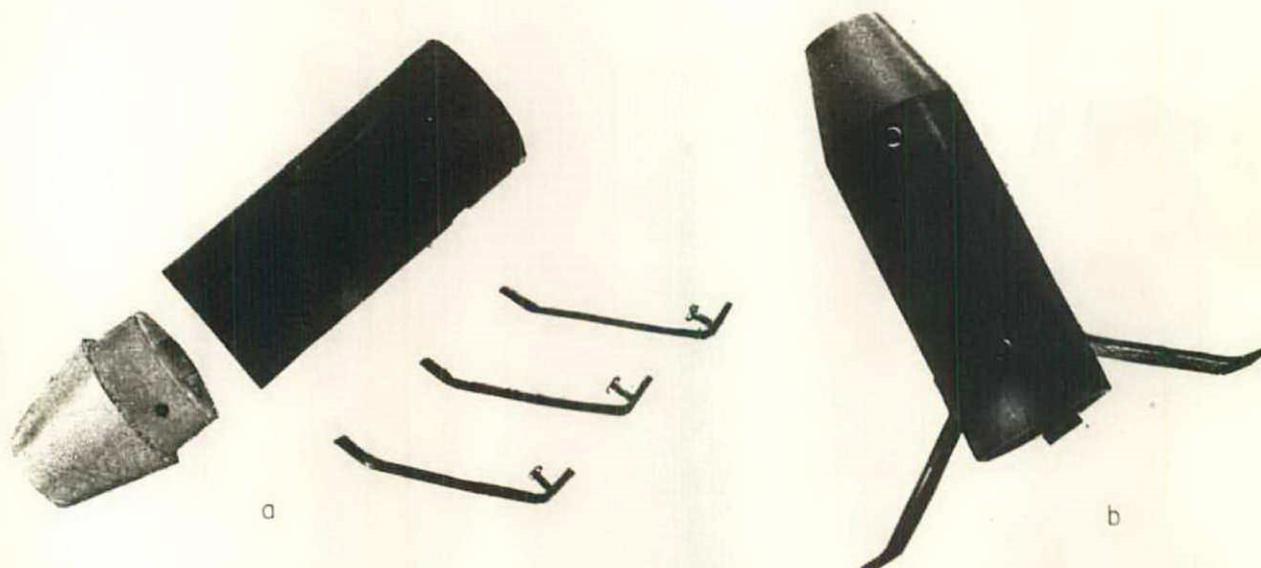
Estrutura de acoplamento capa flexível/carcaça do motor: a) desmontada; b) montada.
